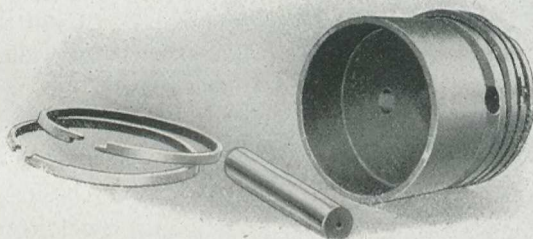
Stoewer, Kolben mit Kolbenringen und -bolzen.
